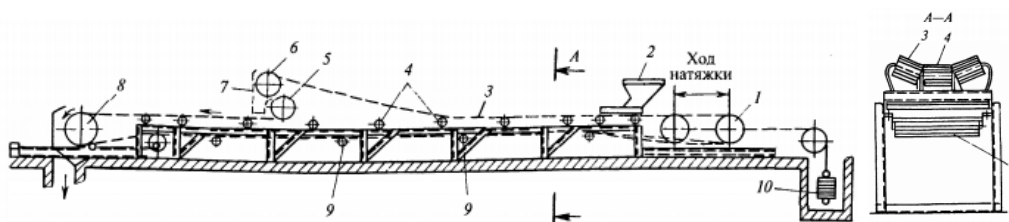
Ленточный питатель: 1 — натяжной барабан; 2 — загрузочная воронка; 3 — лента; 4, 9 — опорные ролики; 5, 6 — барабаны сбрасывателя; 7 — лоток; 8 — приводной барабан; 10 — груз для натяжения ленты
